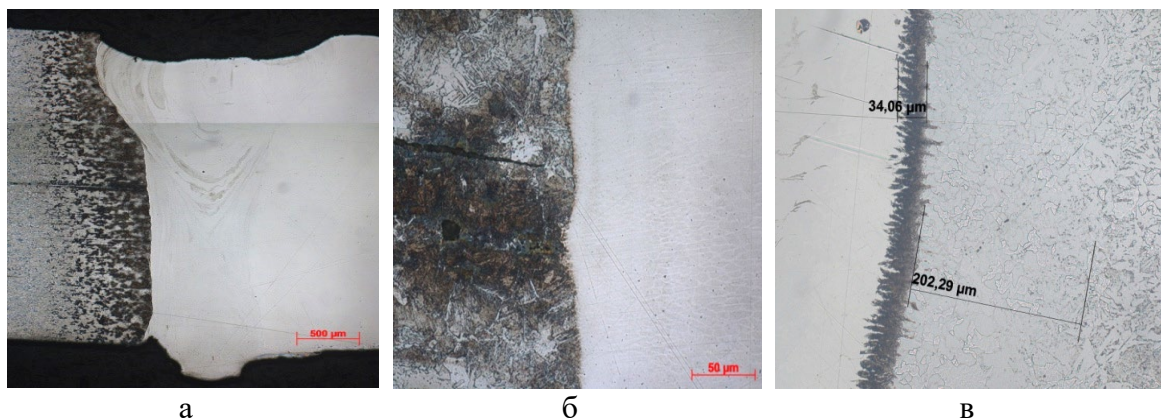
Поперечное сечение разнородного стыкового сварного соединения стали 20 и стали 12Х18Н10Т, полученного ЭЛС (а) и фрагменты линии сплавления со стороны перлитной стали образца после ЭЛС (б) и образца после дополнительной термической обработки (в)
